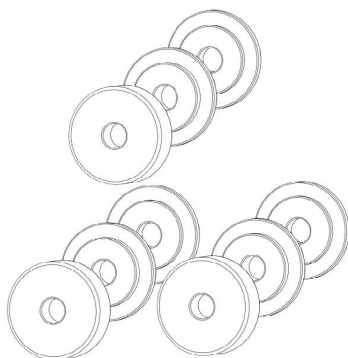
Positionnement des galets par rapport aux axes de la machine
